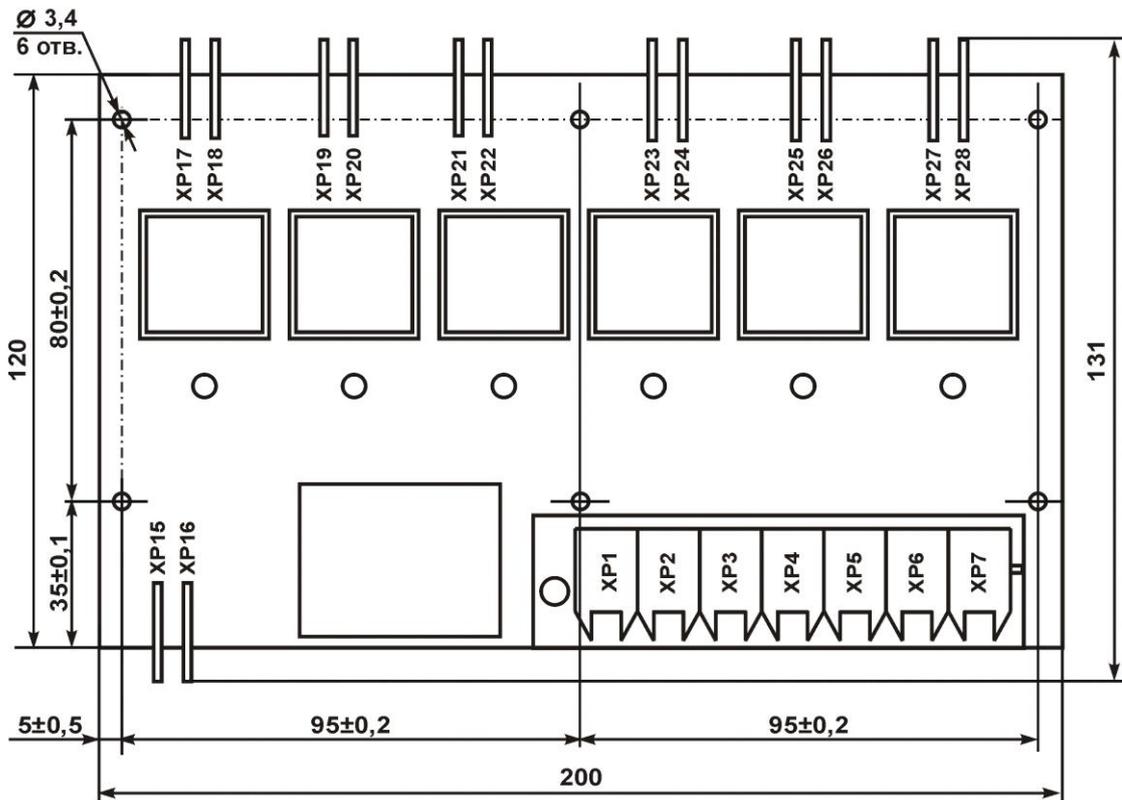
б – Габаритный чертеж ДТ6-О-Бх
